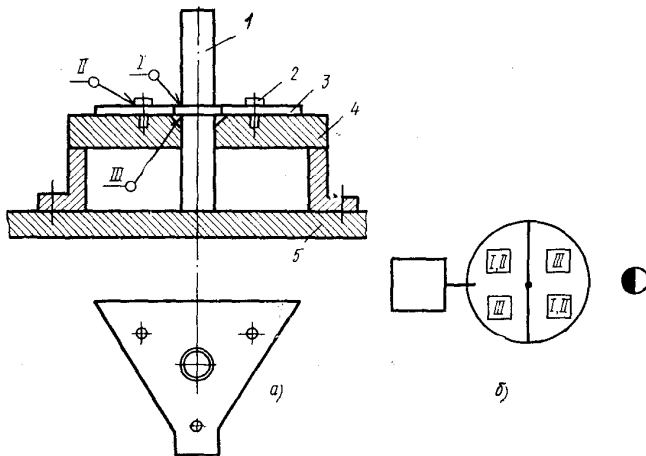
Сборка и сварка фланца с трубой:
